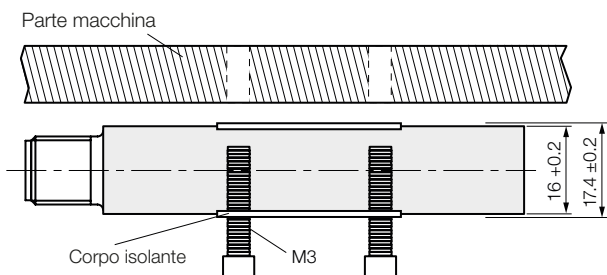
Montaggio della testa sensore con corpo isolante
